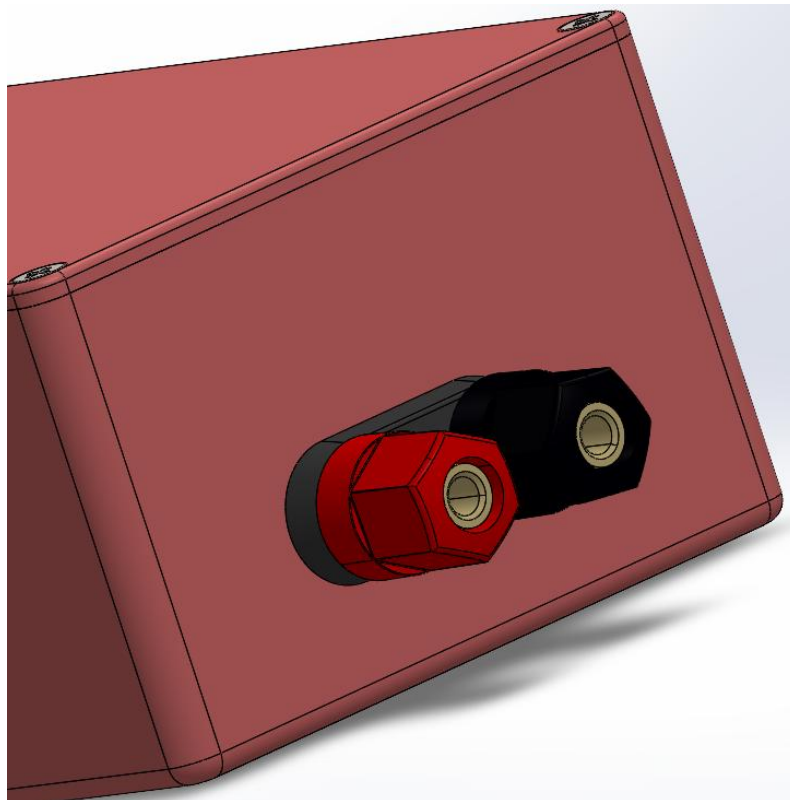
Зовнішній вигляд правої частини корпусу
